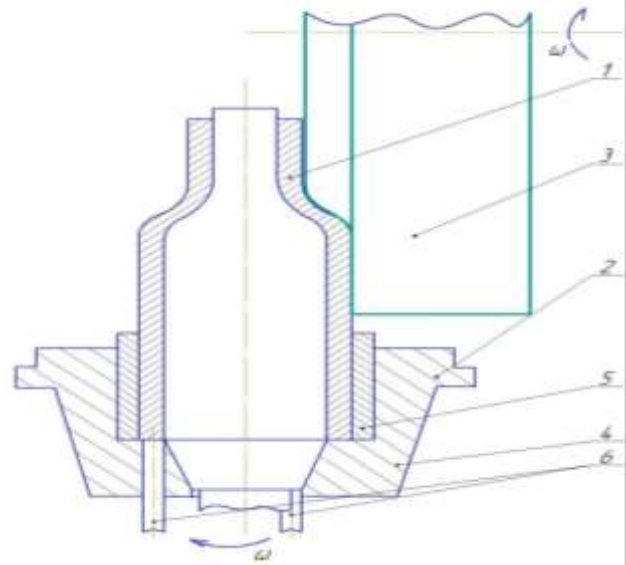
Схема формування горловини трубної заготовки; 1 заготовки, 2 матриця, 3 валок циліндричний, 4 оправка, 5 втулка, штовхачі 6.
